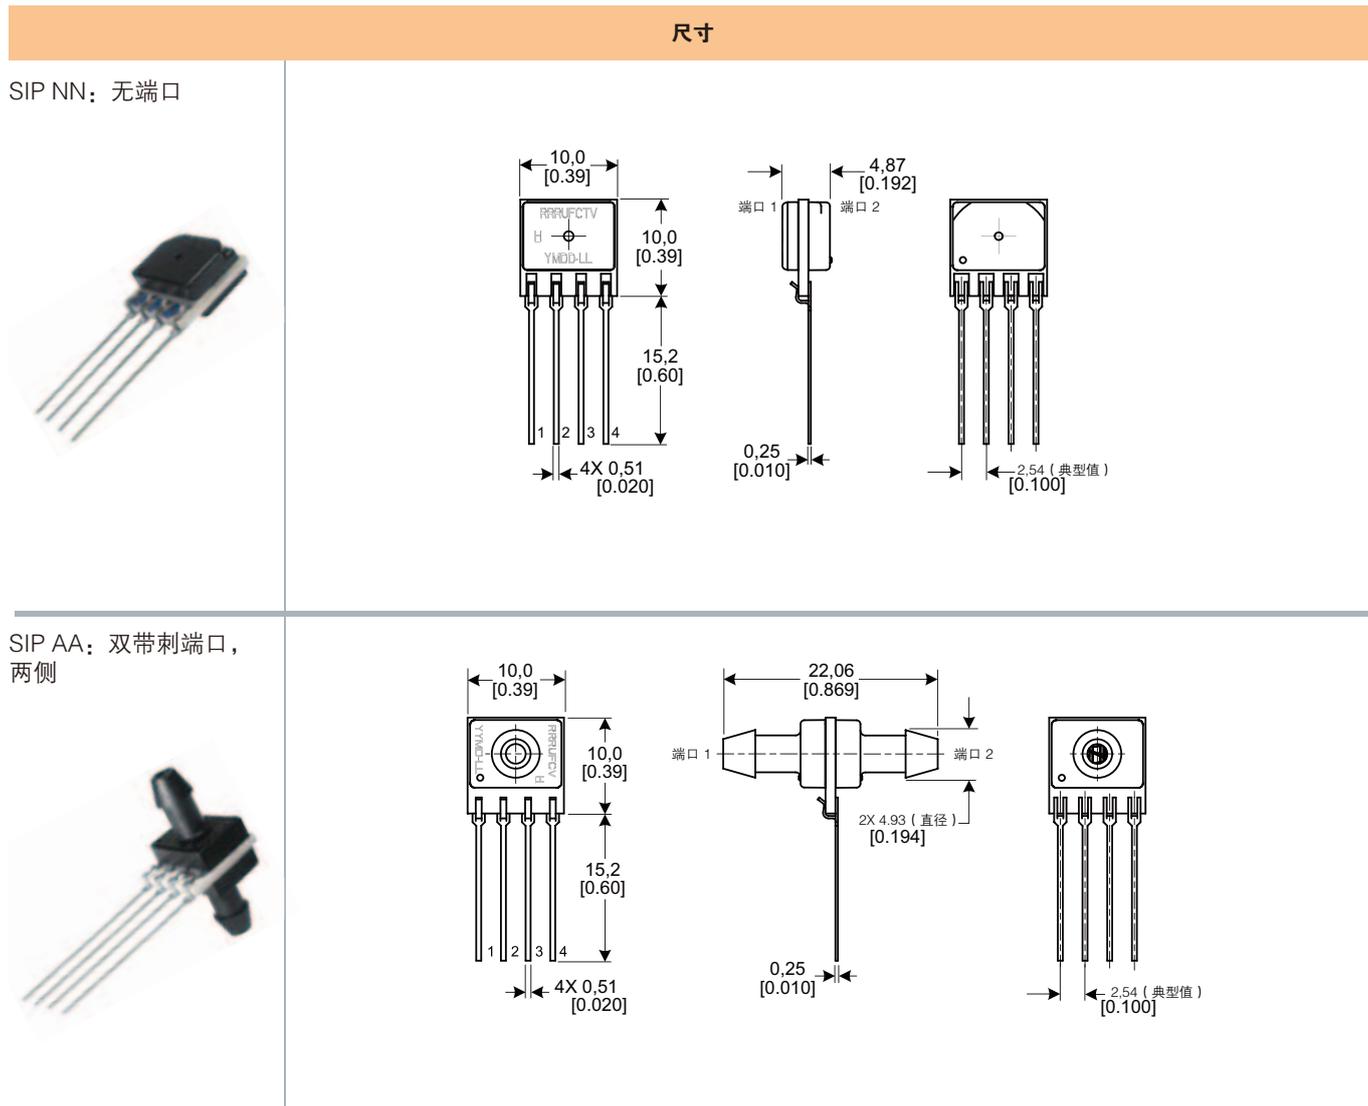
SIP 封装传感器外形尺寸图 (仅作参考, 单位: mm [in])
